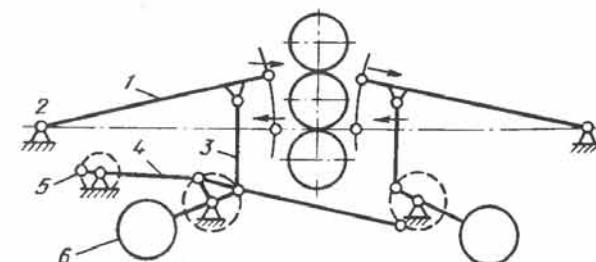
Схема устройства подъемно-качающегося стола трехвалкового сортового стана:
